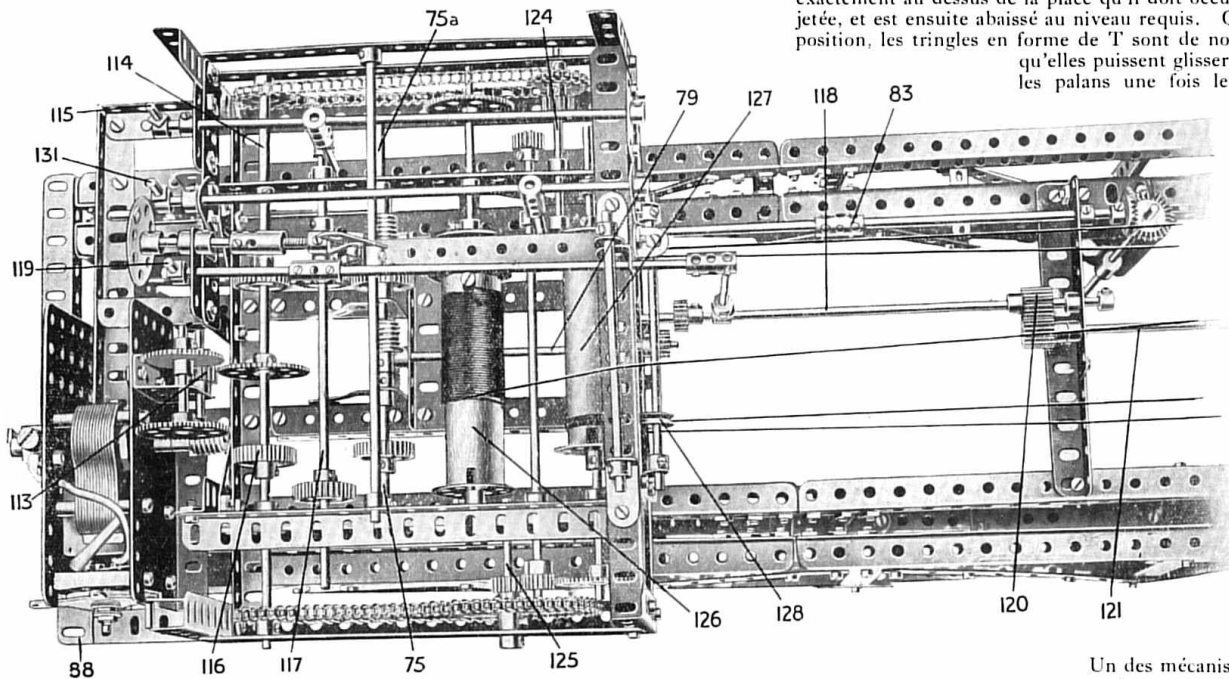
Vue du dessus de la Boîte à Engrenages et du mécanisme adjacent.
